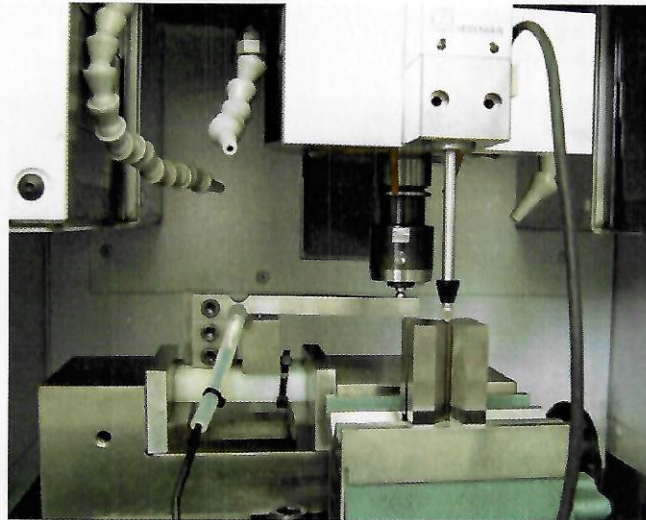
Sistema disparo do sinal de ("Trigger") por contato elétrico instalado no Centro de Usinagem
